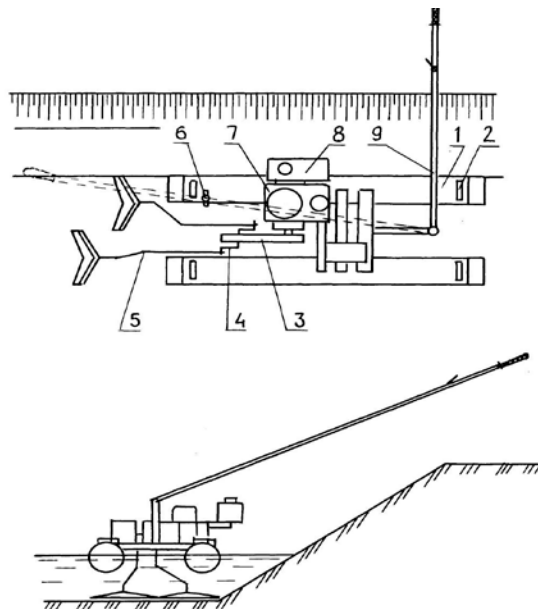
Переносная плавучая косилка: 1 – цилиндрические понтоны; 2 – рукоятки; 3 – передача; 4 – кривошипы; 5 – тяги со стреловидными ножами; 6 – стойка; 7 – двигатель; 8 – топливный бак; 9 – штанга
